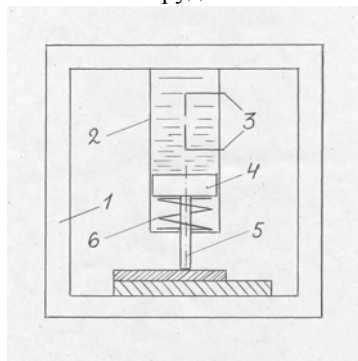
Конструкция сварочного устройства: 1 - рама, 2- цилиндр, 3- электроды с выводами, 4- поршень, 5- ударный шток, 6- возвратная пружина.
